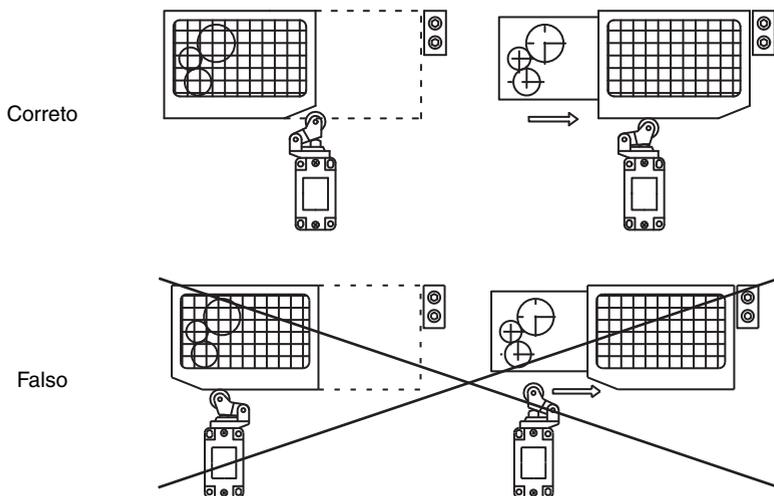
Exemplo de montagem em caso de dispositivo de proteção deslizante
